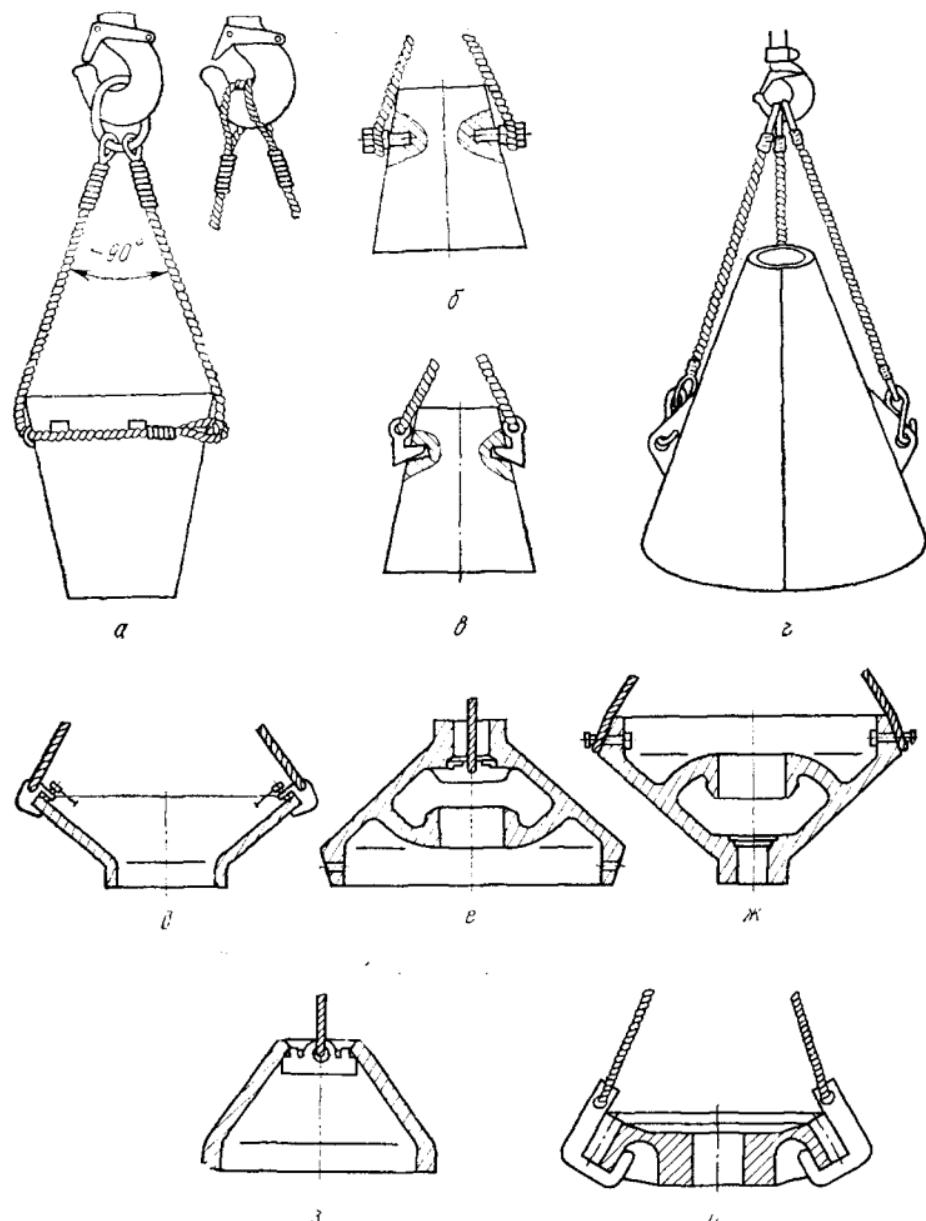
Строповка деталей типа конуса для транспортирования в вертикальном положении:
